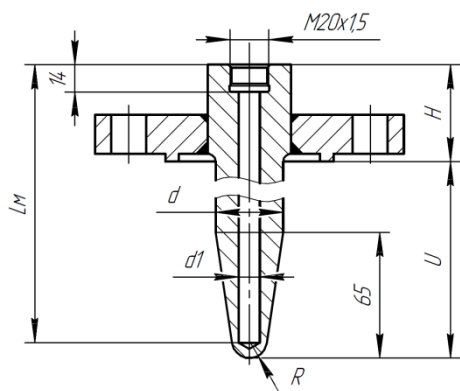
ГТ-714 для ДТ с неподвижным штуцером
